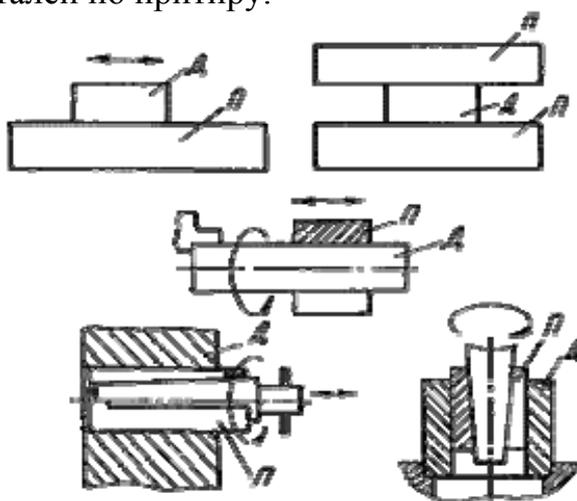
Способы притирки детали: П — притир; Д — деталь
